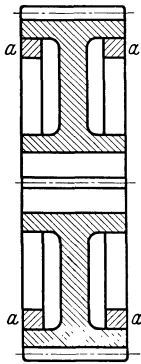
Zahnrad mit eingeschrumpften Dämpferringen a.
